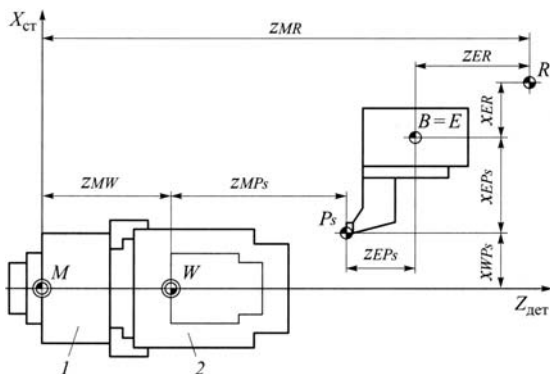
Взаимное расположение нулевой точки детали W , исходной точки инструмента E , исходной точки станка M в системе координат токарного станка $X_c Y_c Z_c$:
